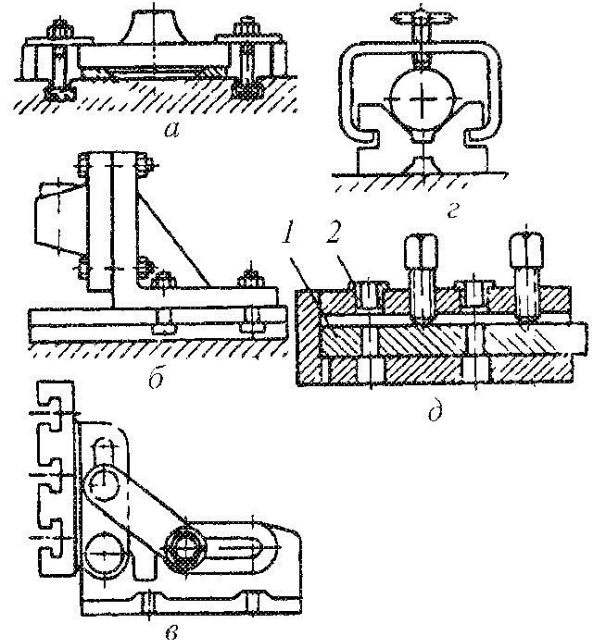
Пристрої для закріплення заготовок на свердильних верстатах
